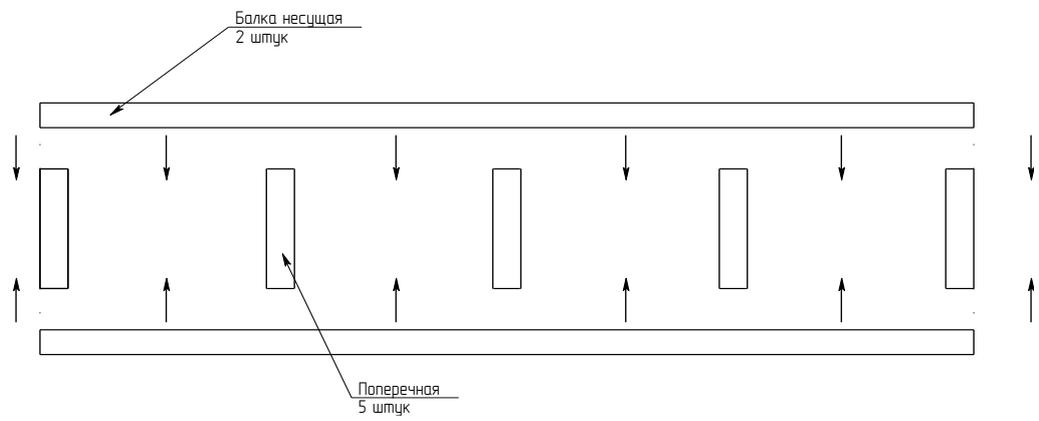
Вид соединения несущей балки и поперечной трубы
